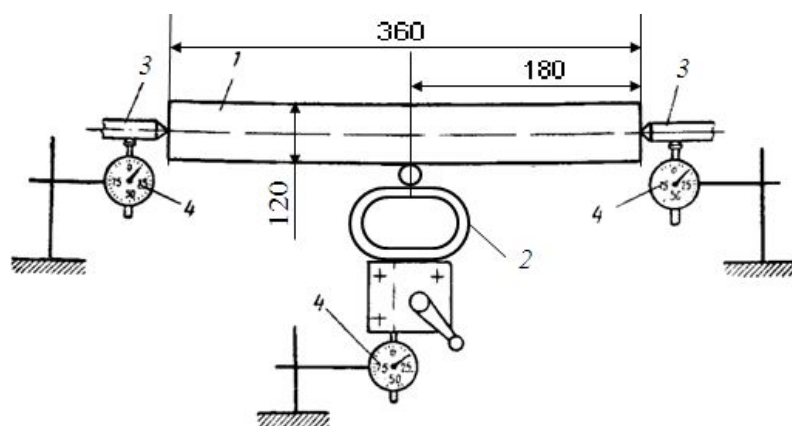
Схема установки для измерения податливости токарного станка при обработке заготовки в центрах: 1 – заготовка; 2 – динамометр; 3 – центры; 4 – индикаторы
